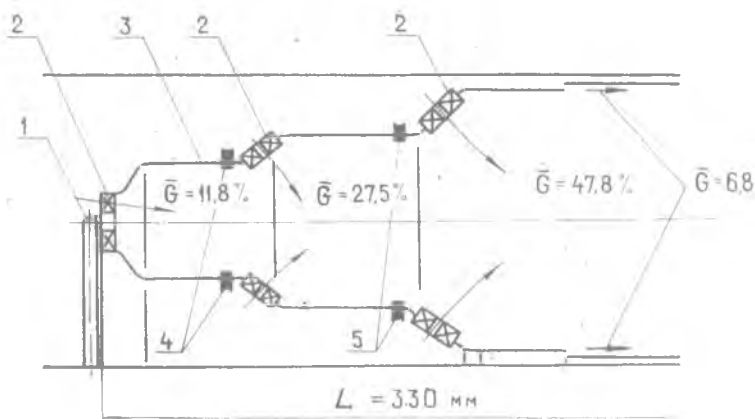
Форсажная камера II контура: 1 — форсунка; 2 — завихритель; 3 — форкамера; 4, 5 — форсунки дополнительного впрыска
